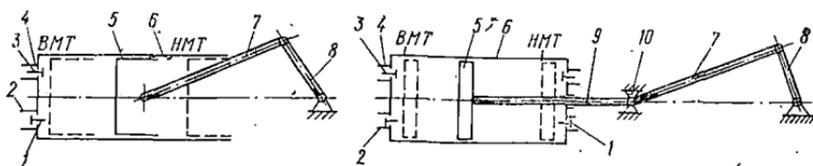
Схемы одноступенчатых поршневых компрессоров
